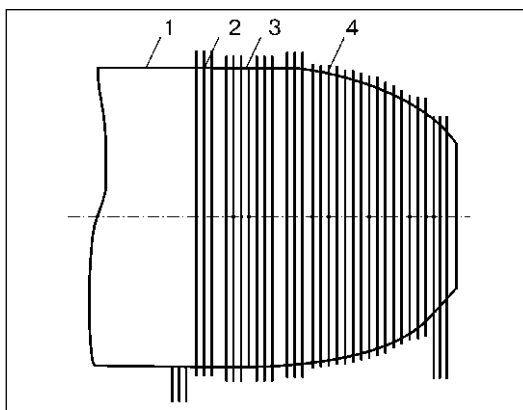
Схема размещения водоохлаждаемого индуктора ВГИК 1000/2,4 на девятой зоне: 1 — цилиндрический участок барабана; 2 — индуктор; 3 — сварной шов; 4 — днище барабана
